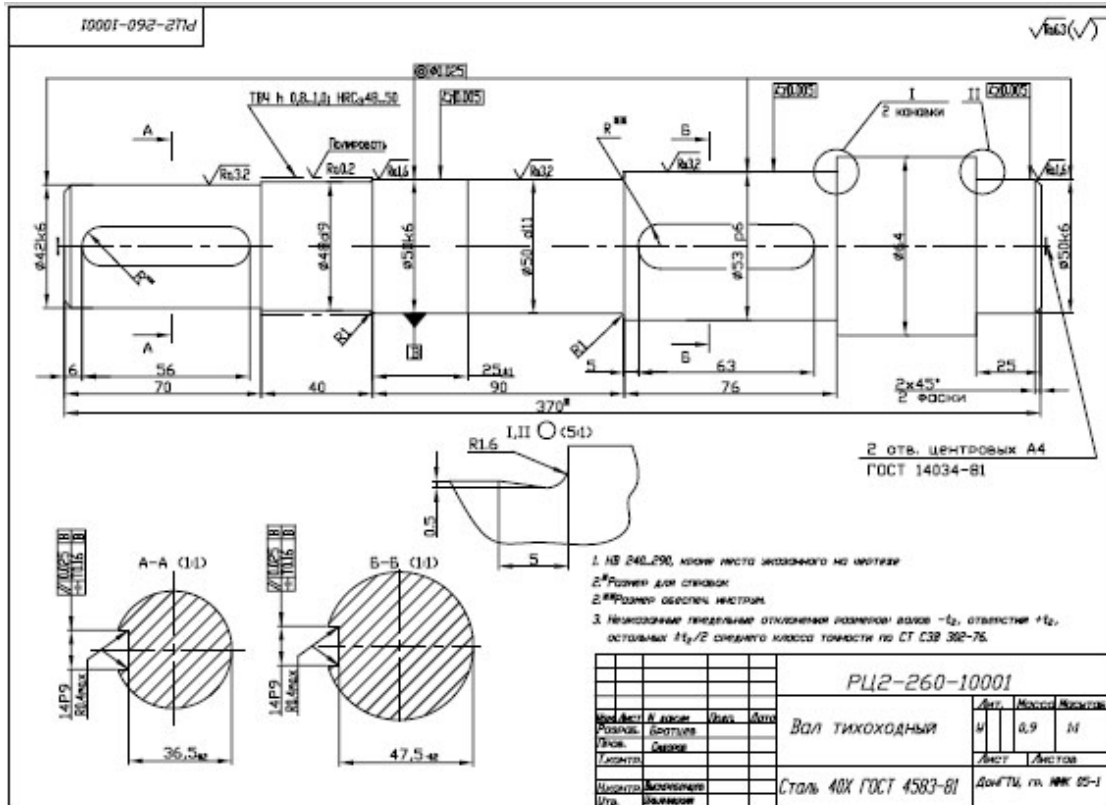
Детализовка вала и зубчатого колеса редуктора (Лист 3)
